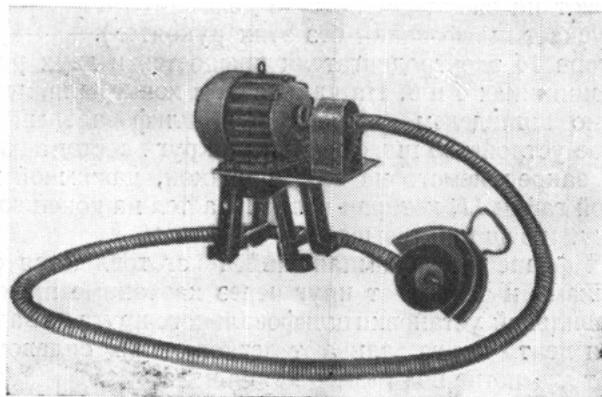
Электрический рельсошлифовальный станок с гибким валом
